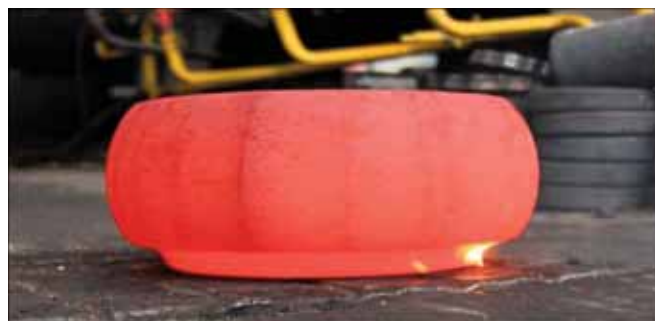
Поковка корпуса турбины после первого перехода штамповки
